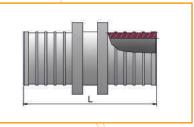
Пресс-муфта соединительная равнопроходная Тип 2
